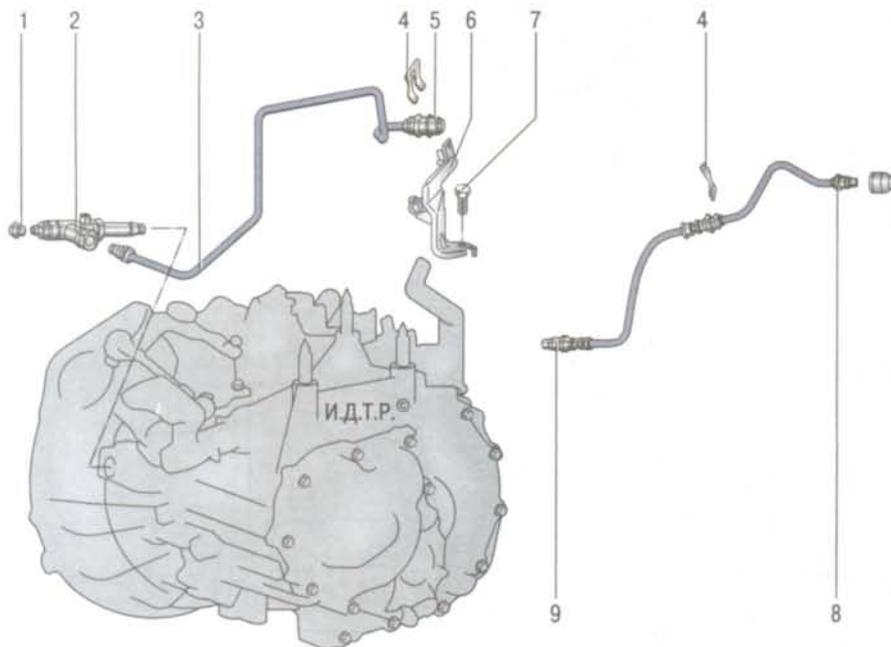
Детали трубопровода гидропривода выключения сцепления: 1 – колпачок штуцера прокачки гидропривода сцепления; 2 – переходник рабочего цилиндра; 3 – шланг гидропривода выключения сцепления; 4 – фиксирующая скоба шланга гидропривода выключения сцепления; 5, 6 – фиксирующие скобы кронштейна трубопровода, установленный на коробке передач; 7 – болт крепления кронштейна трубопровода
